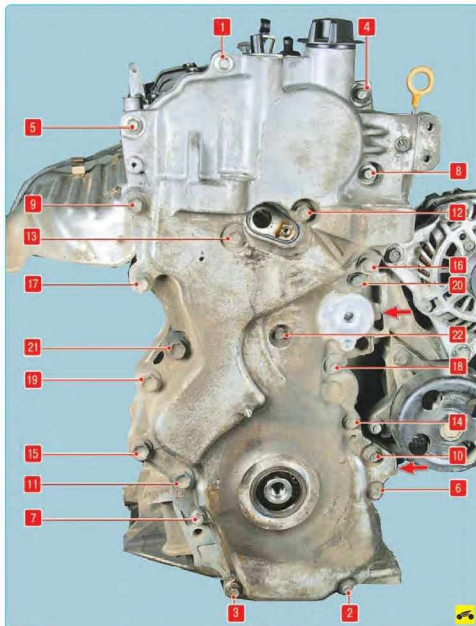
Последовательность выворачивания болтов крепления крышки газораспределительного механизма и места разрезания уплотнителя
